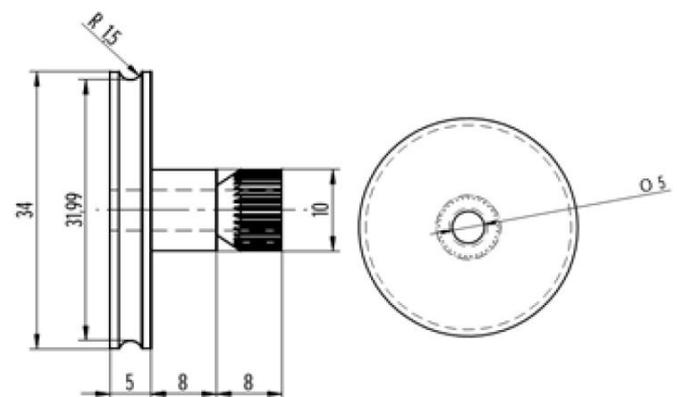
Dimensões para usinagem do tarugo de alumínio valores em milímetros.
